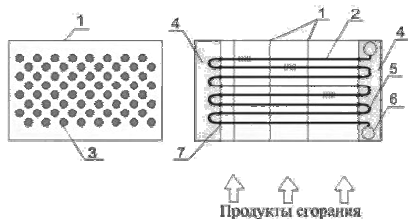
Блок оребренной поверхности нагрева вертикального КУ: 1 – перегородки; 2 – оребренные трубы; 3 – отверстия в перегородках; 4 – боковые боксы; 5 – колесо; 6 – коллектор; 7 – место сварки
